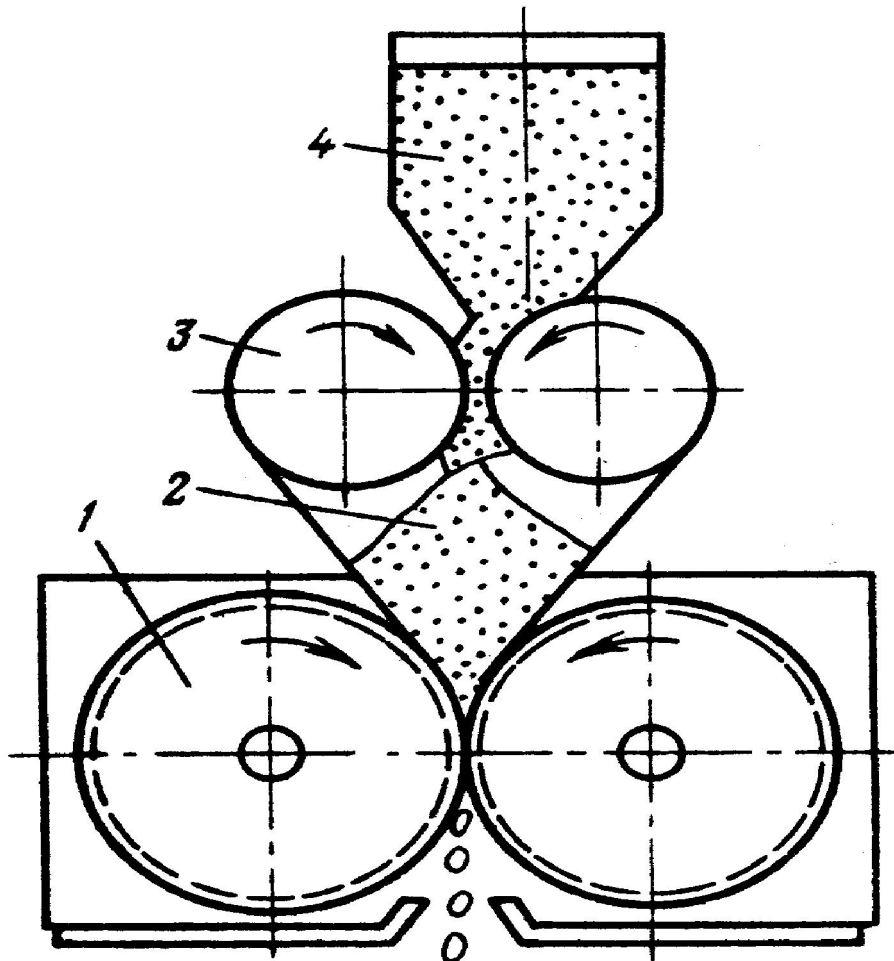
Валковый уплотнитель вальцового пресса
